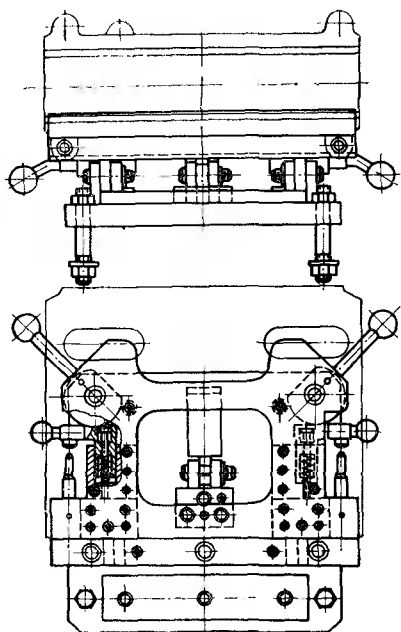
Приспособление для разборки и сборки топливного насоса высокого давления
